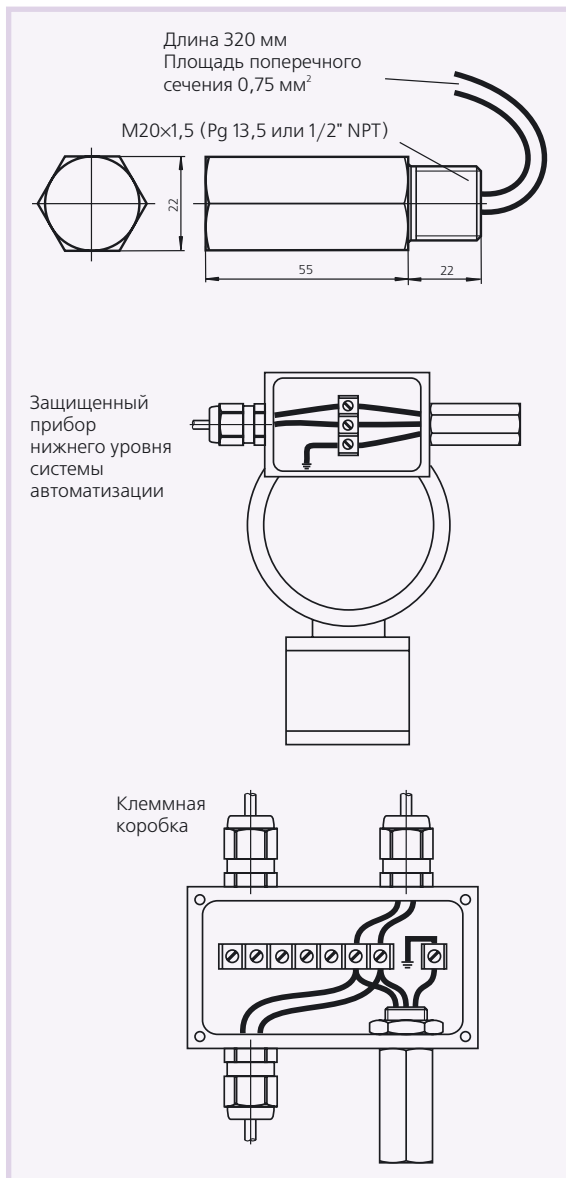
Габаритные размеры устройства F\*-LB-I и примеры схем подключения его внешних цепей при установке устройства на корпусе защищаемого прибора и в клеммной коробке
